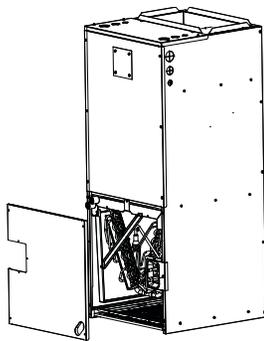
Réinstallez le couvercle de l'évaporateur
